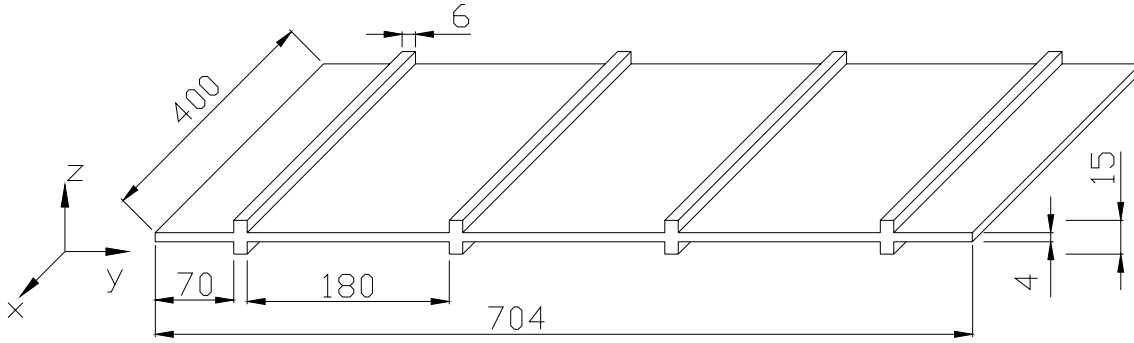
Dimensões do painel reforçado (medidas em milímetros).
